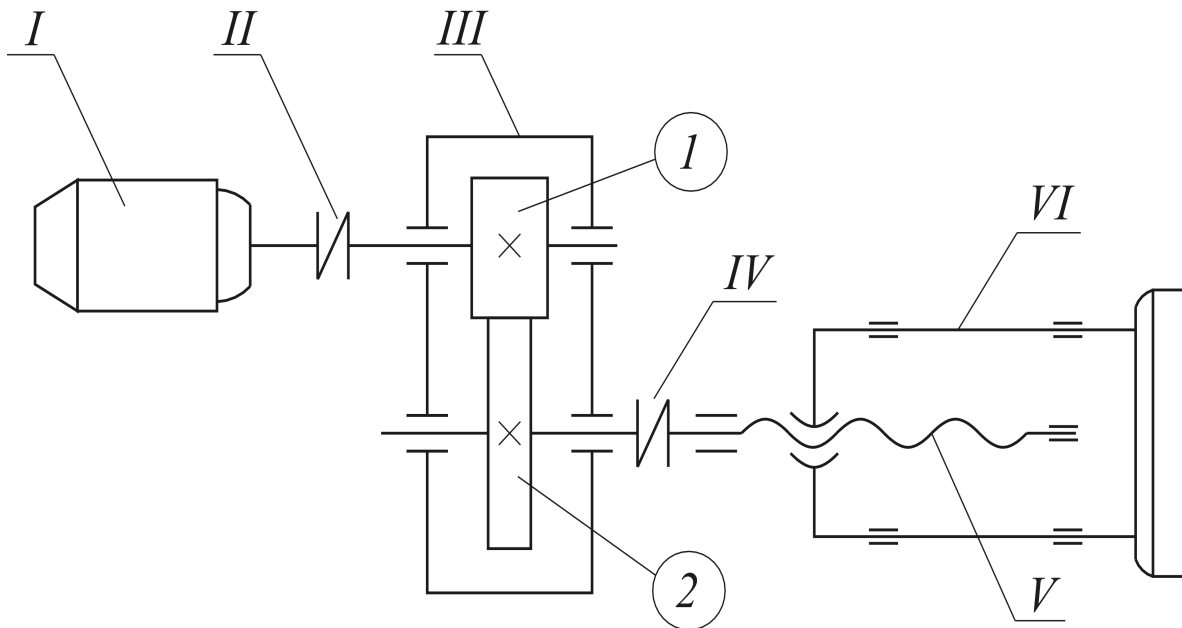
Схема привода: I - электродвигатель; II, IV - муфты; III - редуктор; V - винт толкателя; VI - толкатель
